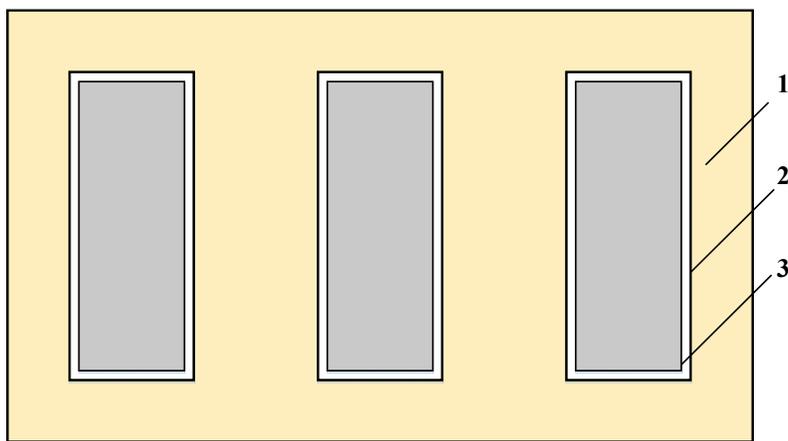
Подставки и охлаждаемые заготовки (вид сверху):
